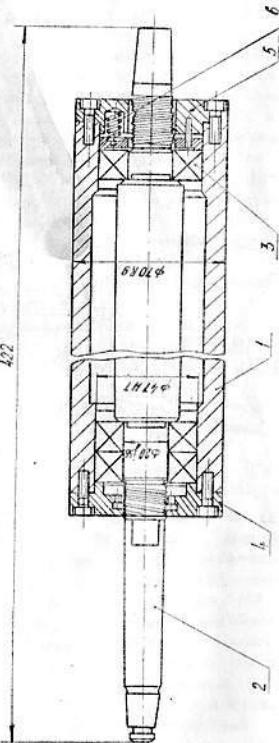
Шиндельный фрезер для обработки молдингов ФУП-3-0.
